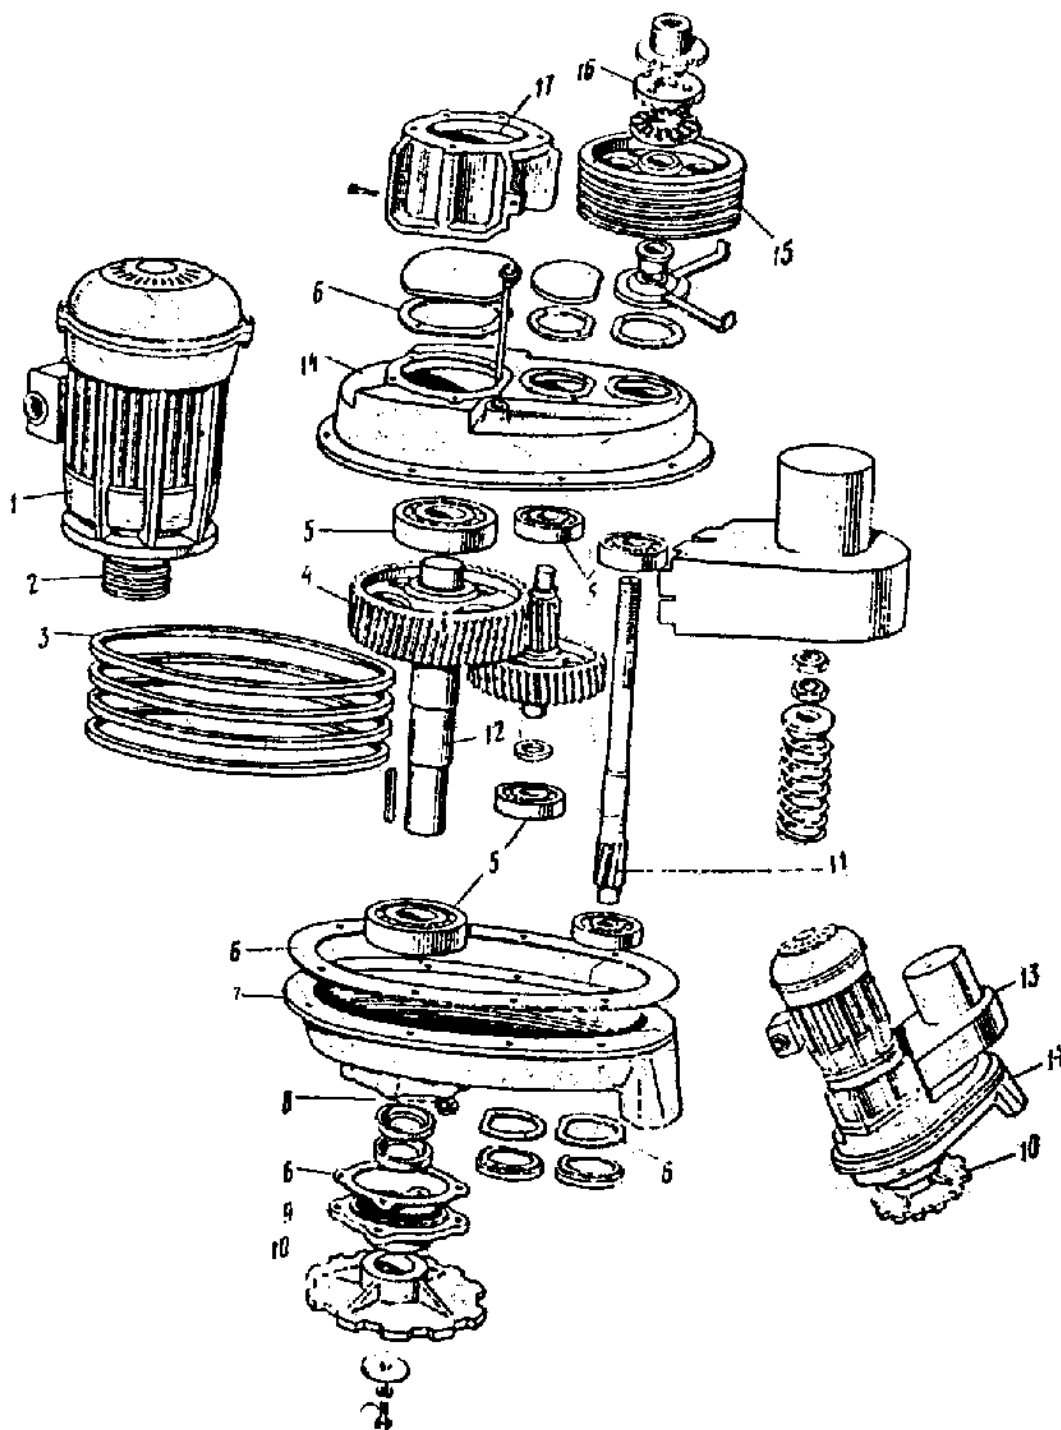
Привідна станція горизонтального транспортера КСТ–8 (ТСН–3,0Б):1–електродвигун; 2–шків малий; 3 –паси клинові; 4 –зубчата передача; 5- підшипники кочення; 6 –прокладка; 7 –корпус редуктора; 8- зливна пробка; 9 –кришка підшипника; 10 –ведуча зірка; 11 –перший вал; 12 - другий вал; 13 –кожух; 14 –кришка редуктора; 15 –великий шків; 16 –муфта храпова; 17 –стакан
